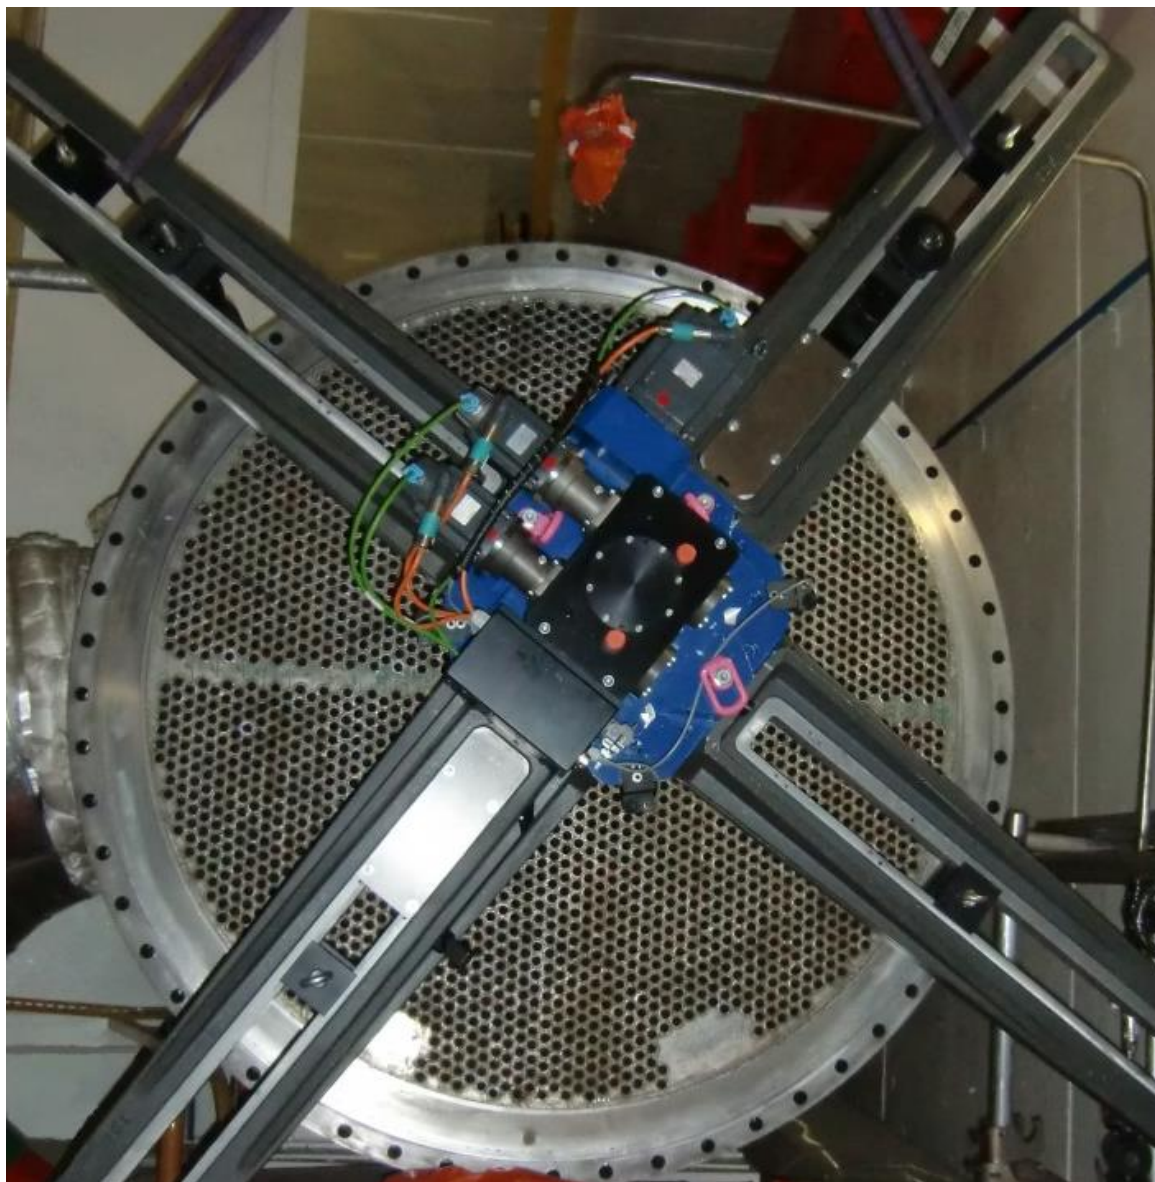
Zobrazení úprav pro možnost obrábění tepelného výměníku systému TQ.
